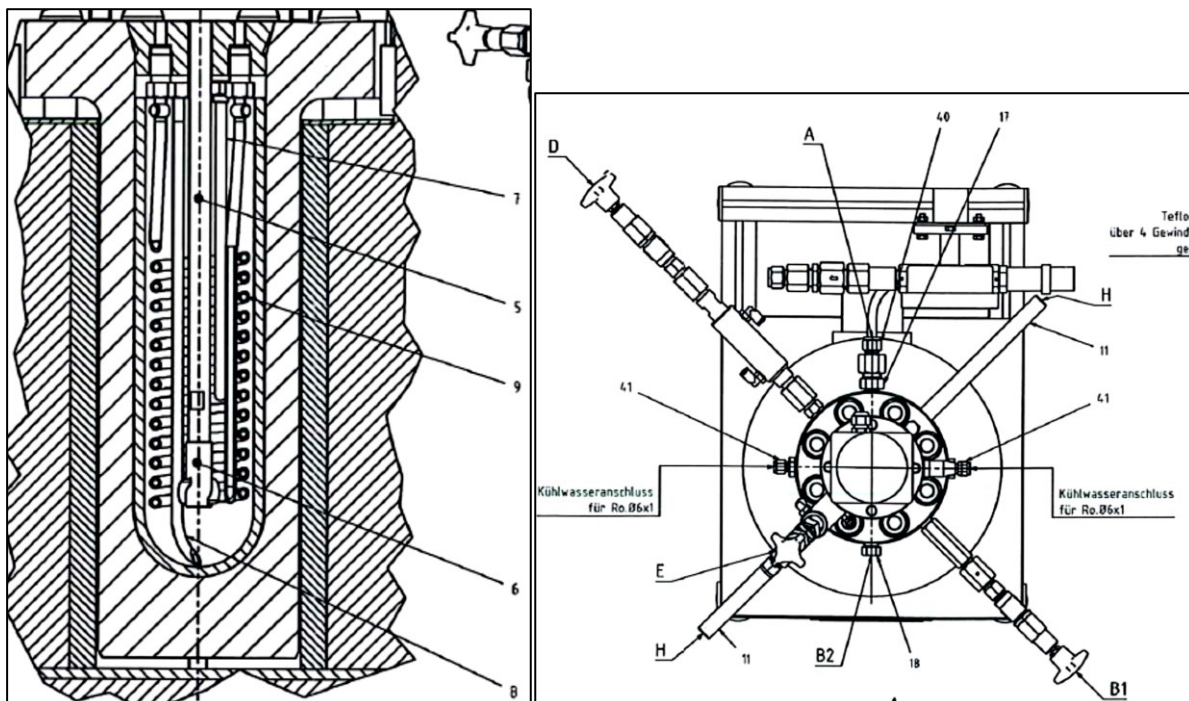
Detailausschnitt der Bombe mit Einbauten (links), Grundriss des Autoklaven (rechts)
